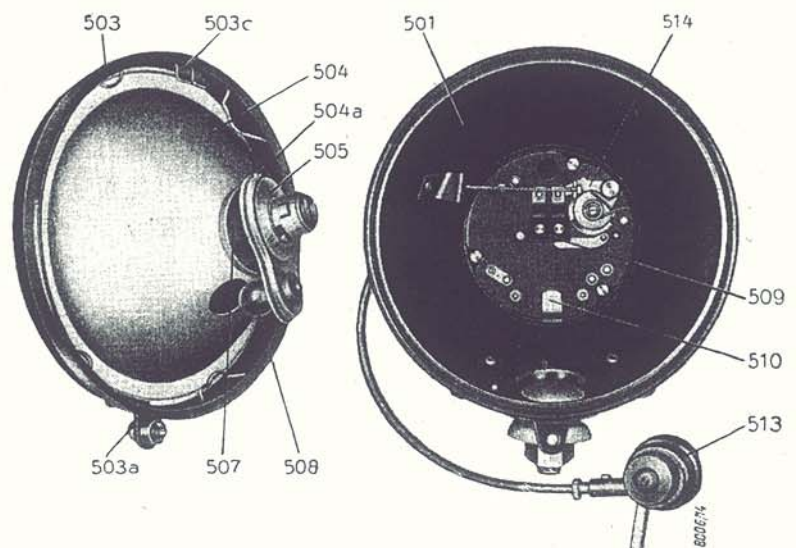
Scheinwerfer geöffnet zum Auswechseln einer Glühlampe
